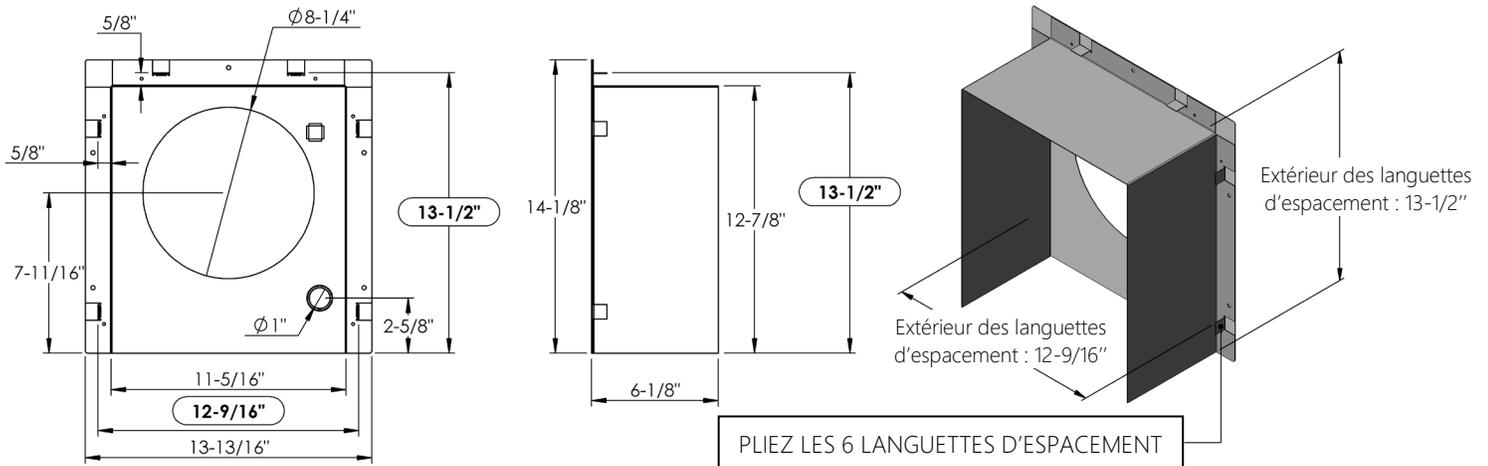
Dimensions générales du manchon mural du PVH58FM.
